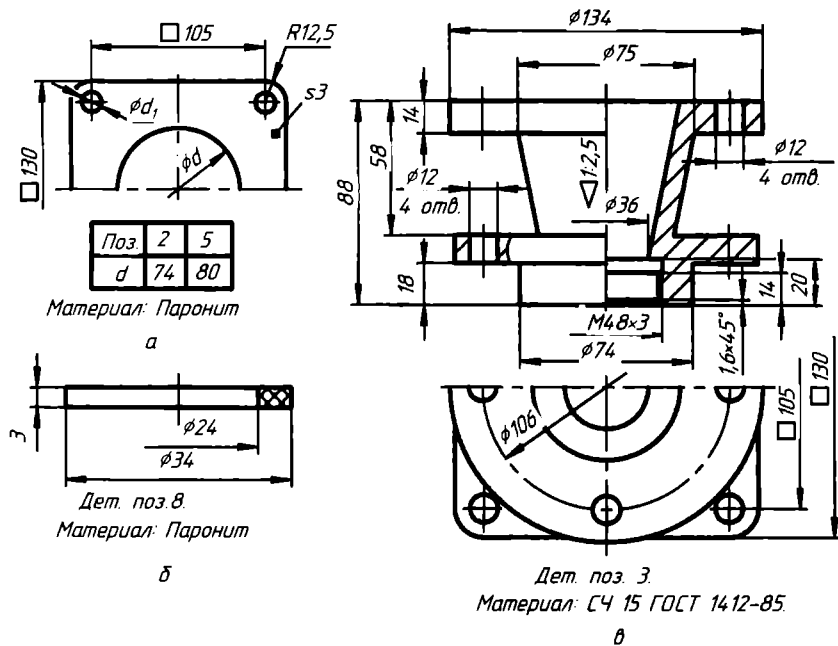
Чертежи: а, б — прокладка; б — патрубка впуска
